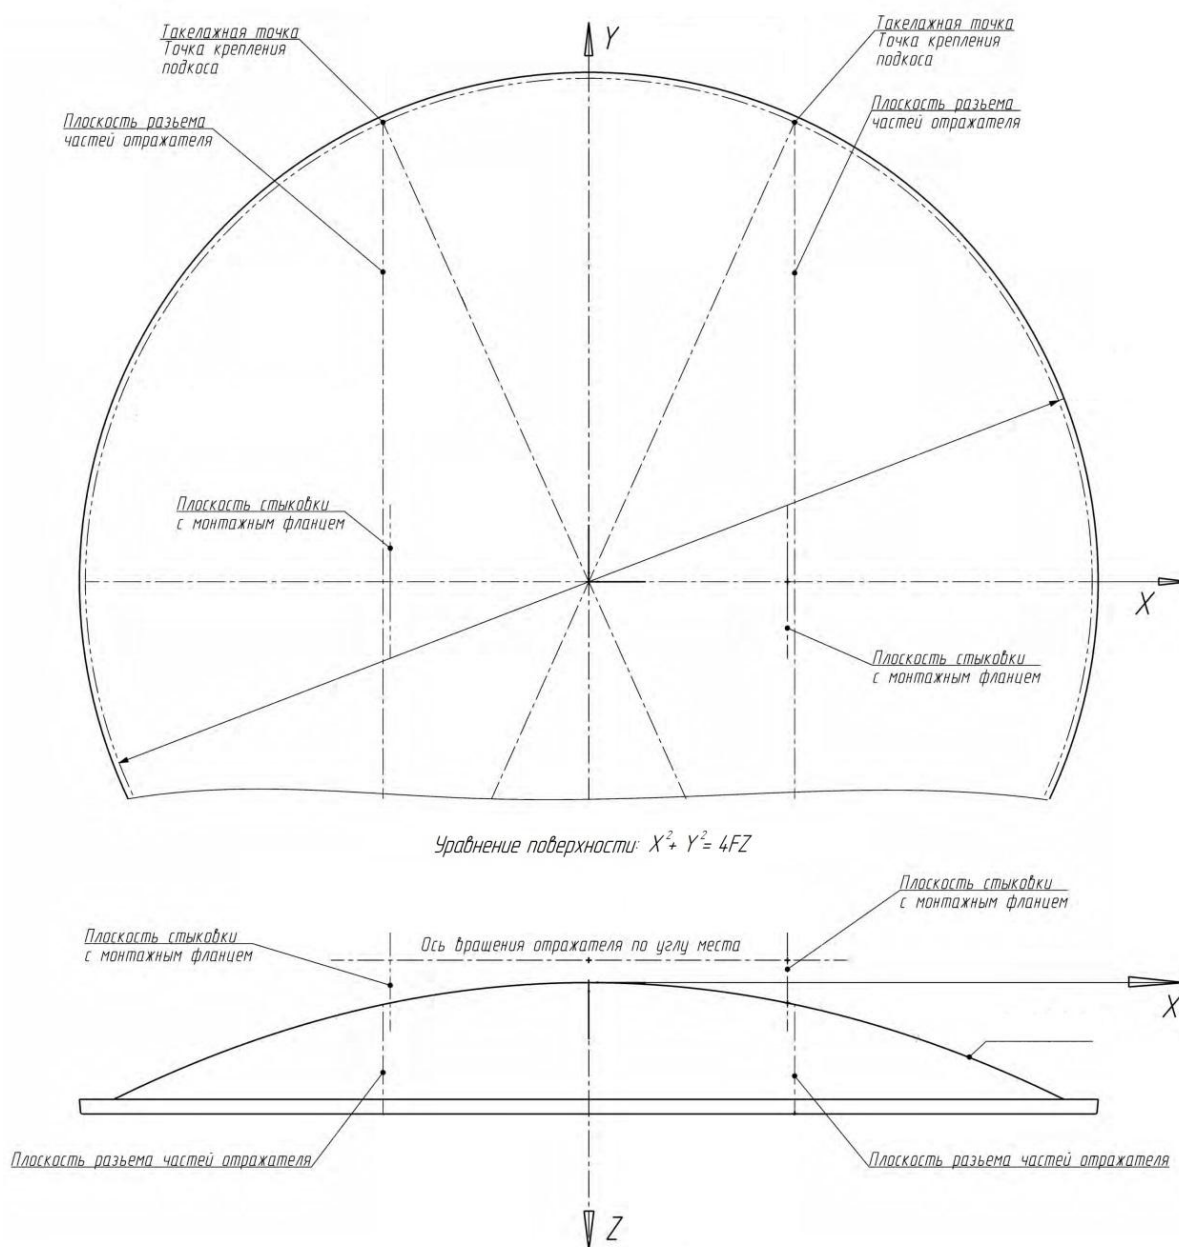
Геометрическая схема разбора отражателя и закрепления на опорно-поворотном устройстве.
